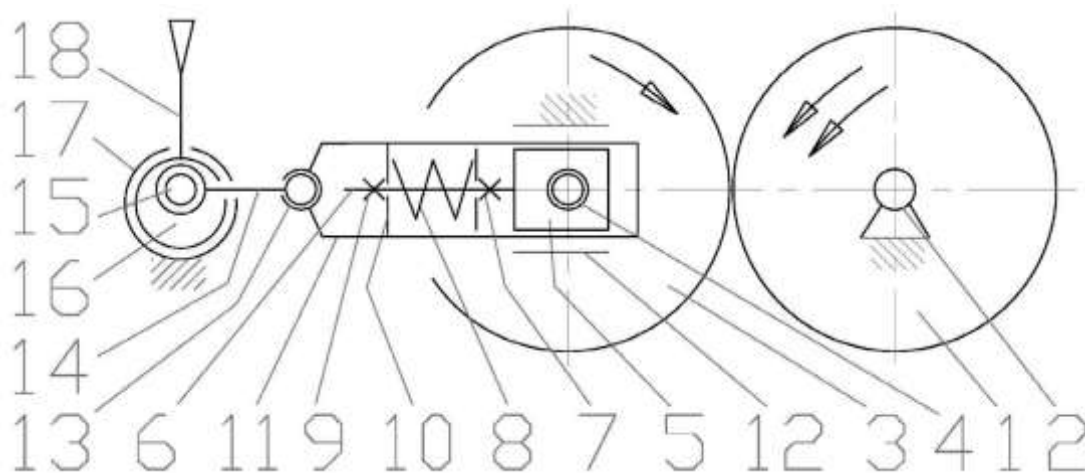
Схема вальцьовий дробарки фірми DAVIS.
